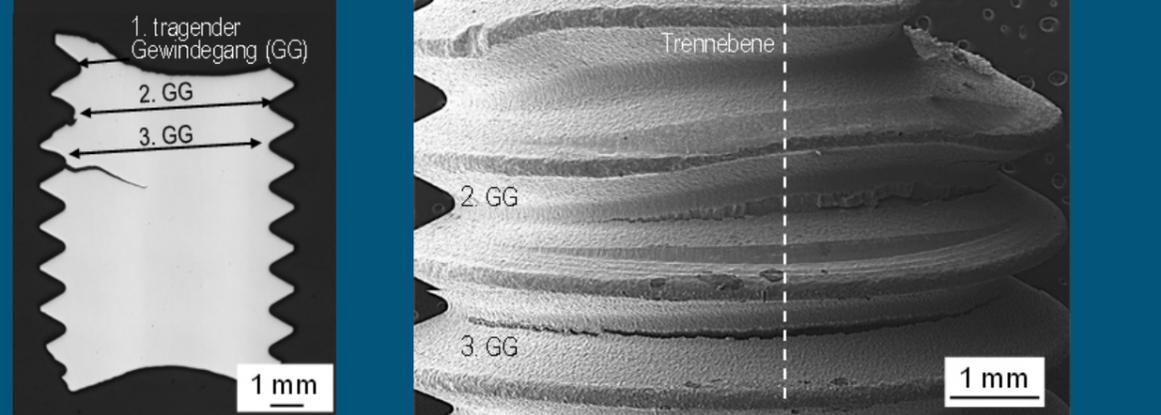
Metallografisches Schlibbild einer geölten Schraubenverbindung, (links) makroskopische REM-Aufnahme, (rechts) Anrisse in den ersten drei Gewindegängen.
